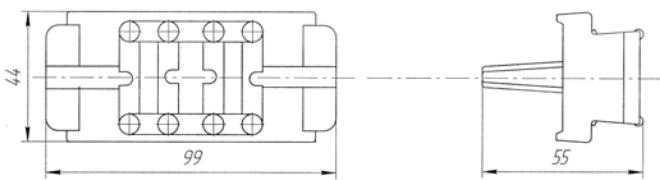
Габаритные размеры штепселя типа ШК 4М
